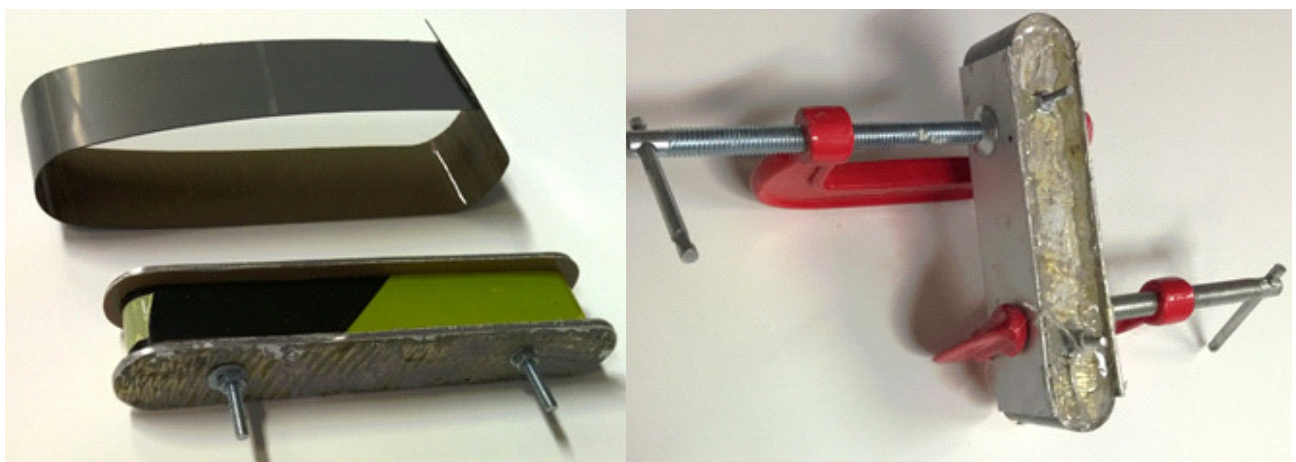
Fabrication des premières bobines entièrement inorganiques.
